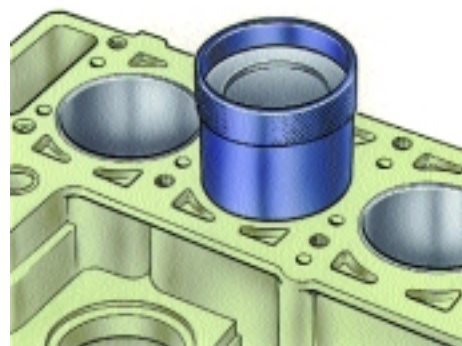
Установка поршня с поршневыми кольцами в цилиндр двигателя мод. 2106-70 с помощью втулки из набора
